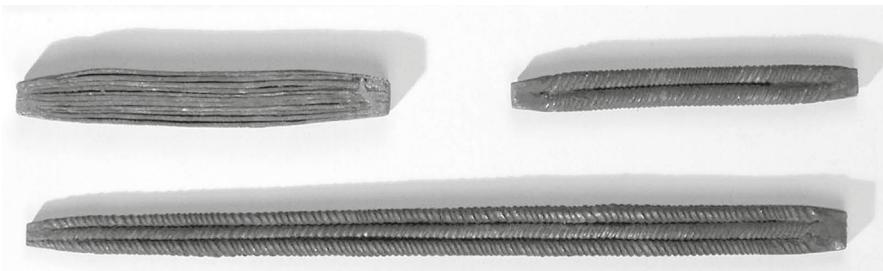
Заготовки для клинков из дамаска из «Технического кабинета»:
